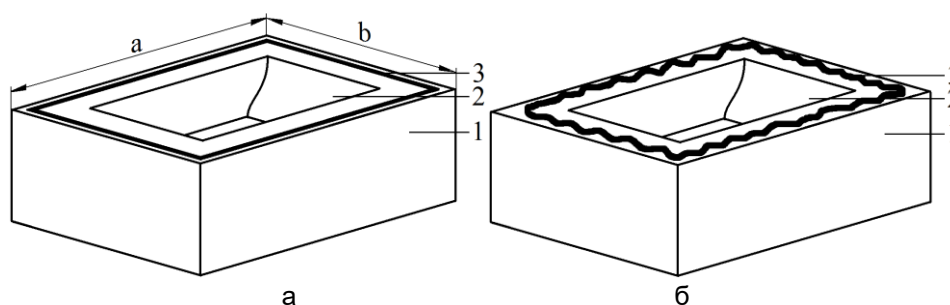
Схема нанесення прямолінійного (а) і зигзагоподібного (б) клейового шва на сполучаються частини форми: 1 – пів-форма; 2 – робоча порожнина пів-форми; 3 – клейовий шов
